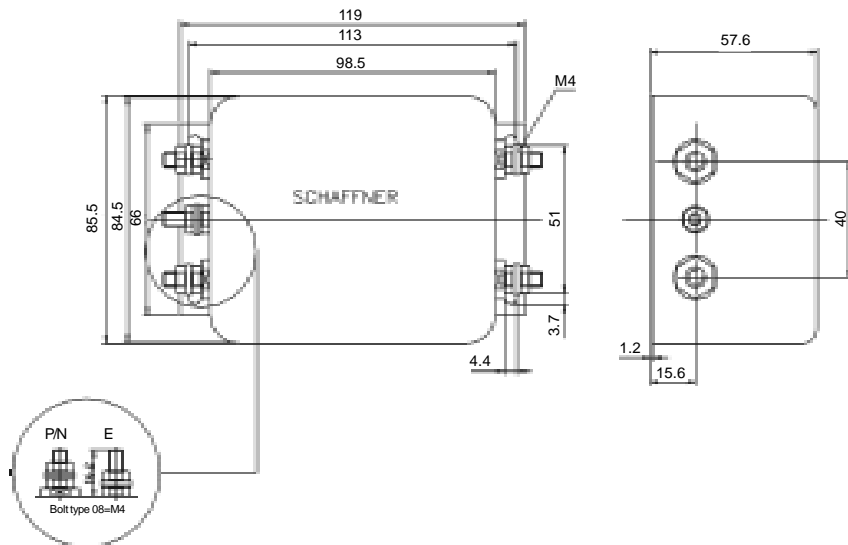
Чертеж внешнего фильтра FS6007-36-08 и FS6007-25-08
